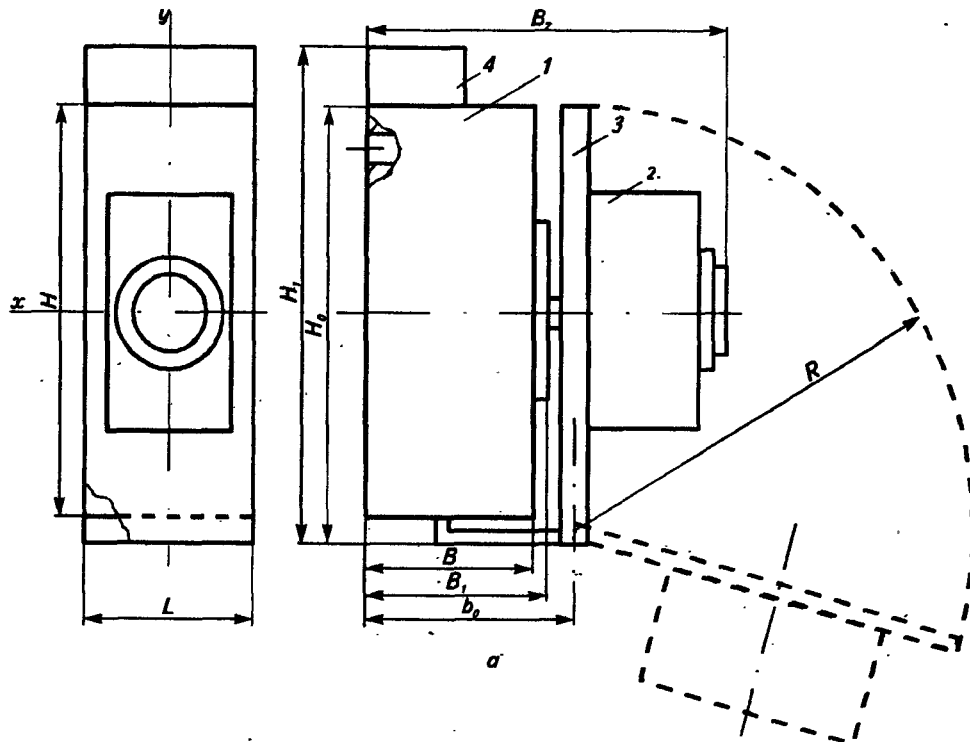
Габаритный чертеж выключателей стационарного исполнения с электромагнитным приводом
